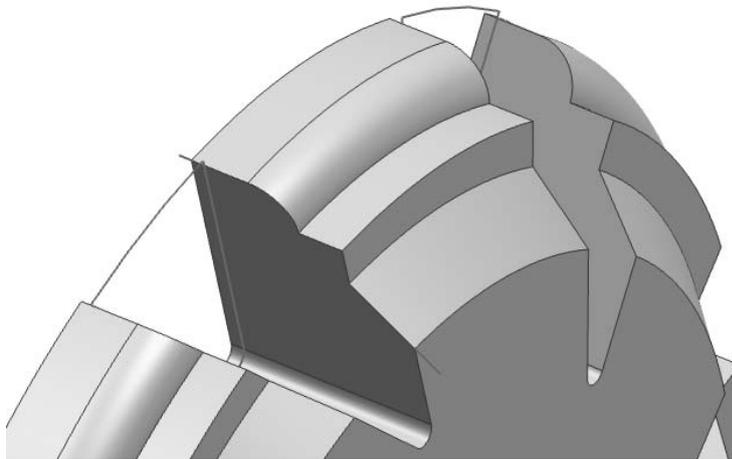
Схема удлинения режущей кромки фасонной фрезы
